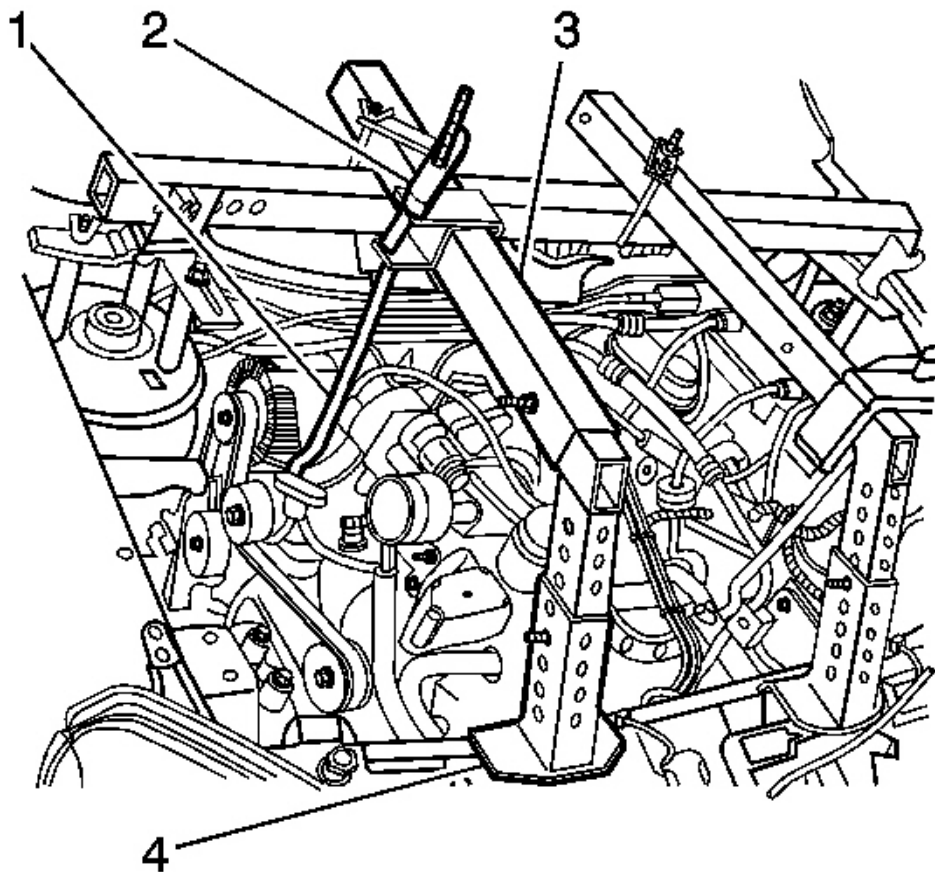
Posicionamiento J 28467-7A elevadores de gancho en el motor trasero Cortesía Ascensor soporte de General Motors Corp.
